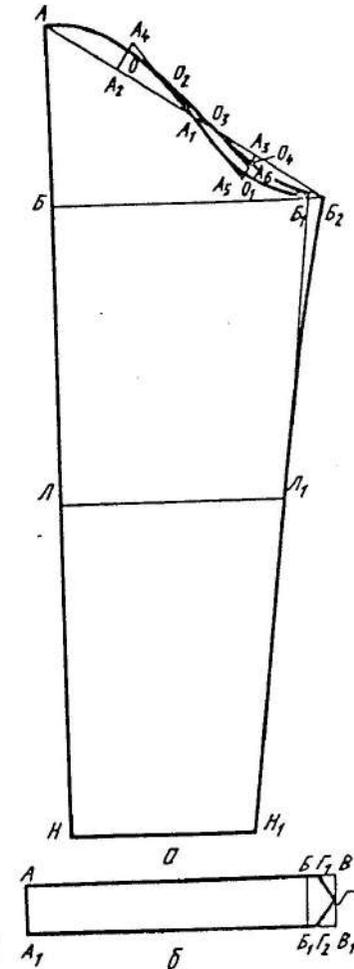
Чертеж рукава рубашечного типа с манжетой
